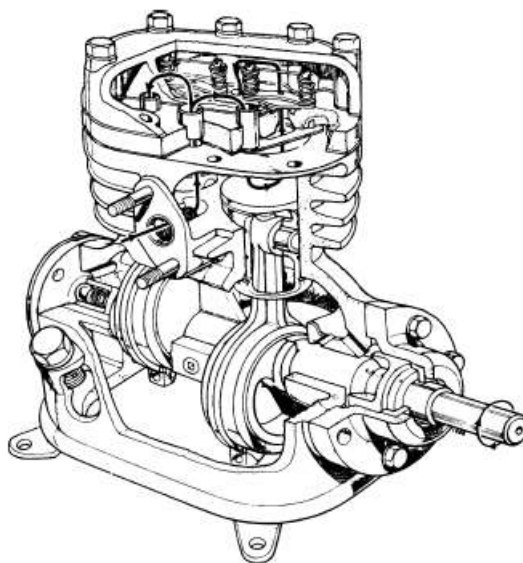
Assemblaggio di un compressore alternativo a due cilindri
